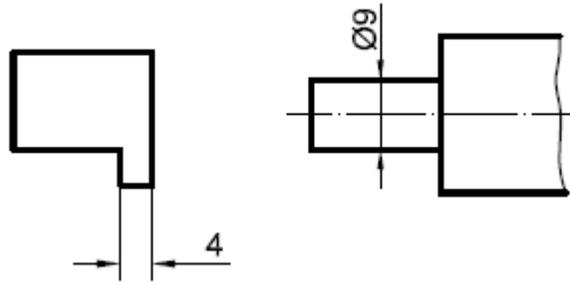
Colocación de la cifra de cota cuando la dimensión acotada sea muy pequeña.
